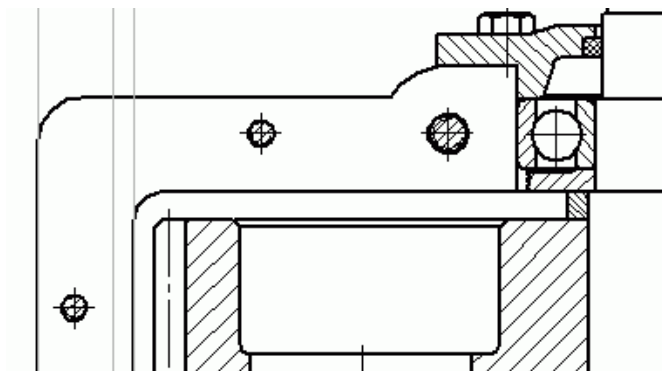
Вспомогательные линии для построения корпуса редуктора
